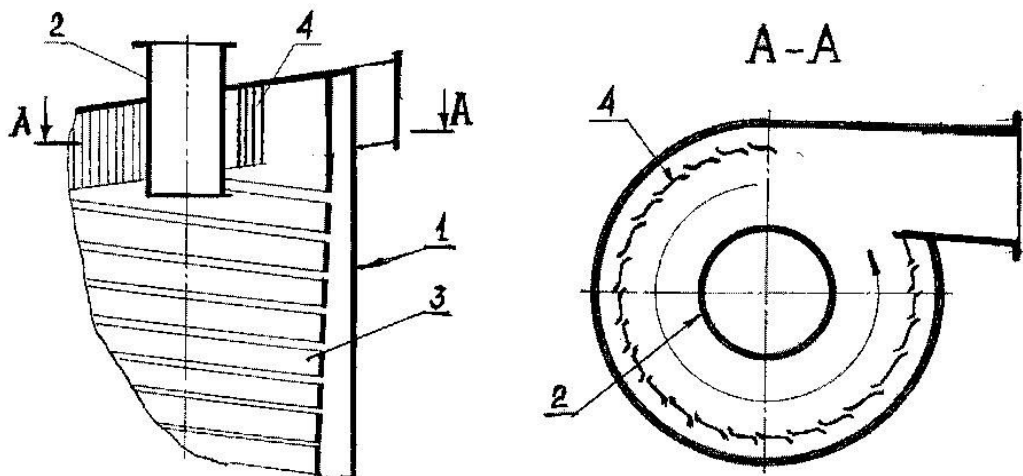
Конструктивне оформлення вторинного завихрителя: 1 – корпус; 2 – вихідний патрубок; 3 – конічна гвинтова сепараційна камера; 4 – жалюзійний розвантажувач.
